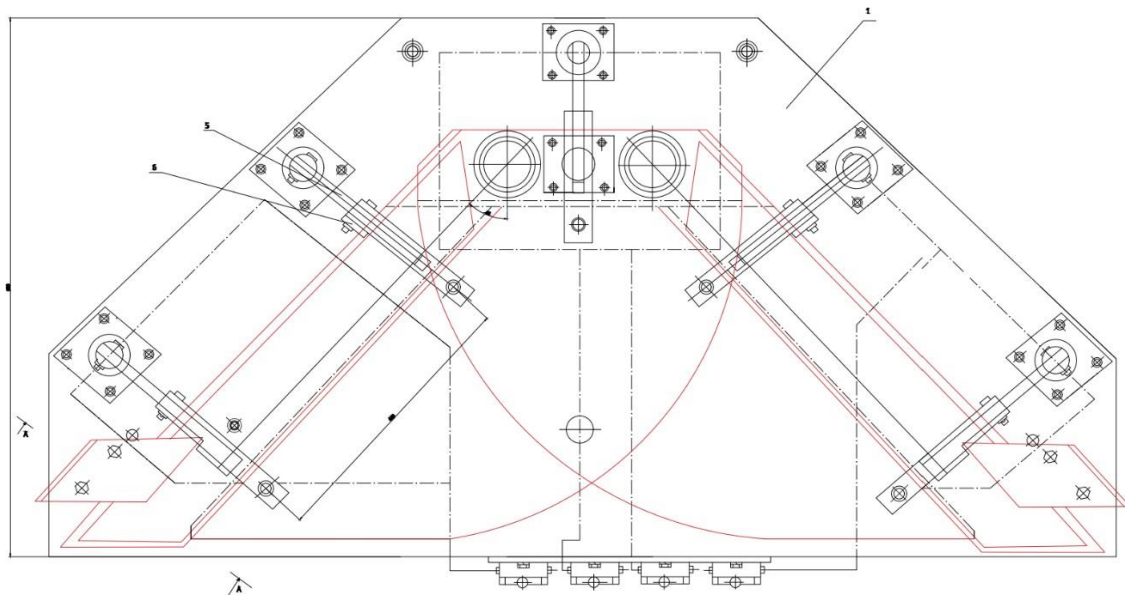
Кондуктор для зварювання і складання боковин .
